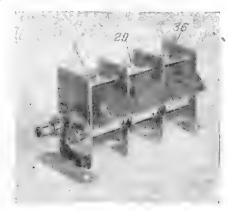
Коиденсаторный агрегат приемника АИ-656
